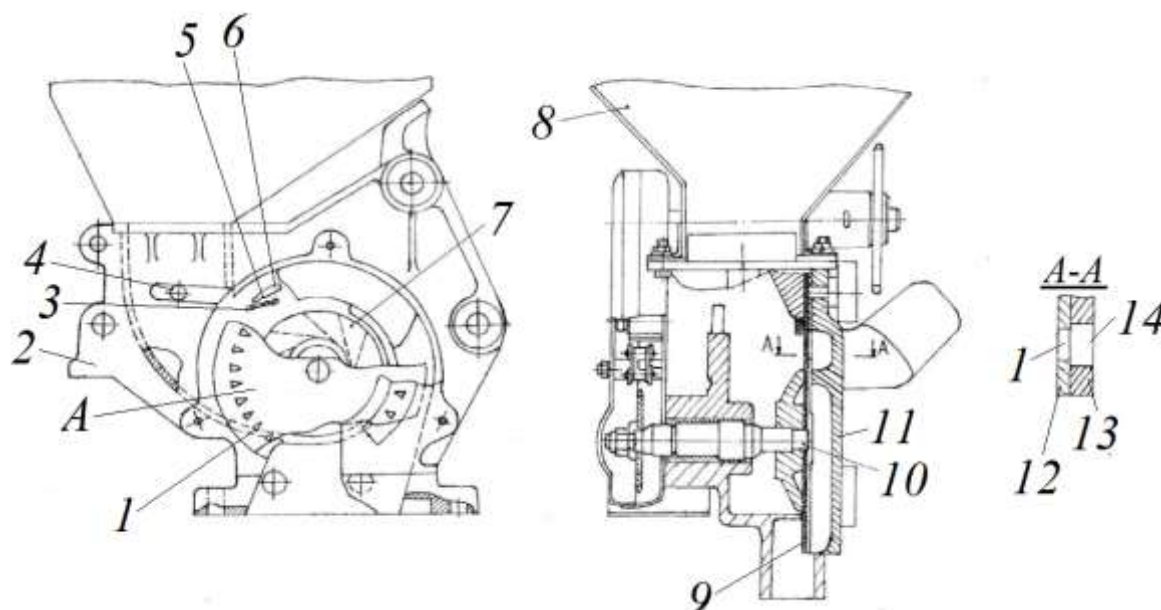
Пневматичний висівний апарат вакуумного типу: А – висівний диск; 1 – трикутний отвір; 2 – корпус; 3 – вилка скидача; 4 – механізм регулювання; 5 – робоча поверхня виступу; 6 – напрямник; 7 – ворушилка; 8 – бункер; 9 – прокладка; 10 – вал; 11 – кришка; 12 – накладка; 13 – основа; 14 – круглий отвір.
